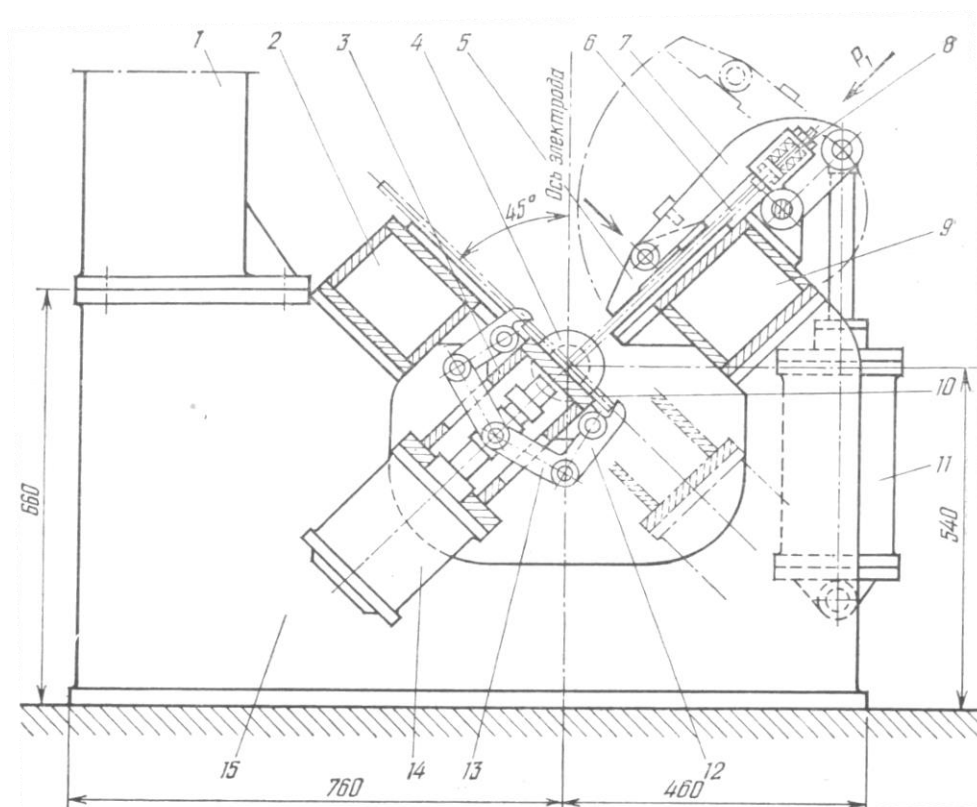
Кондуктор – кантователь для сборки и сварки тавровых балок
